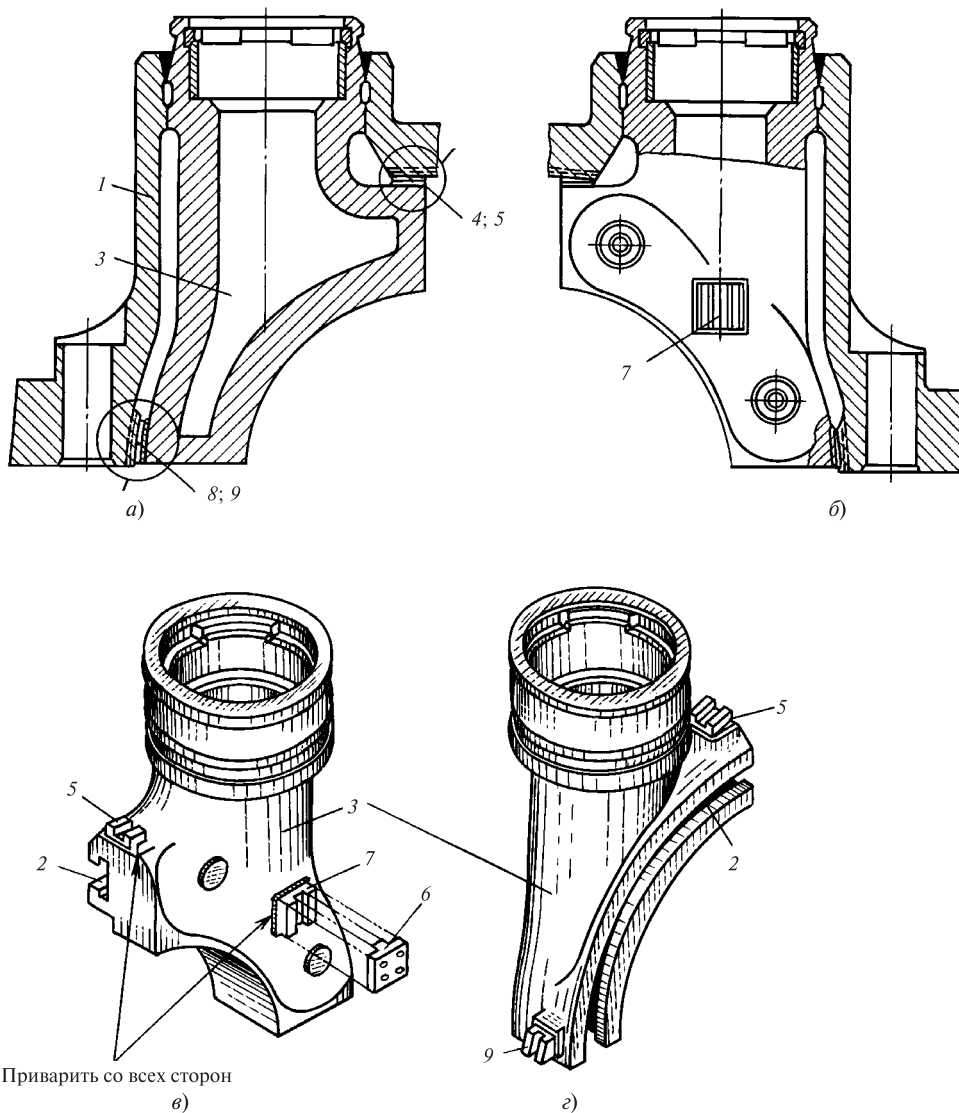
Двухстенный корпус ЦВД турбины Т-250/300-23,5 ТМЗ
